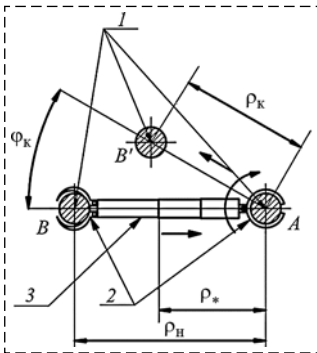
Расчетная схема поворотно-заклинивающего движителя:
